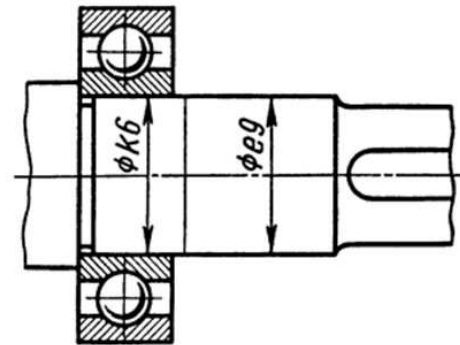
Крепление внутреннего кольца подшипника на валу посадкой с натягом
